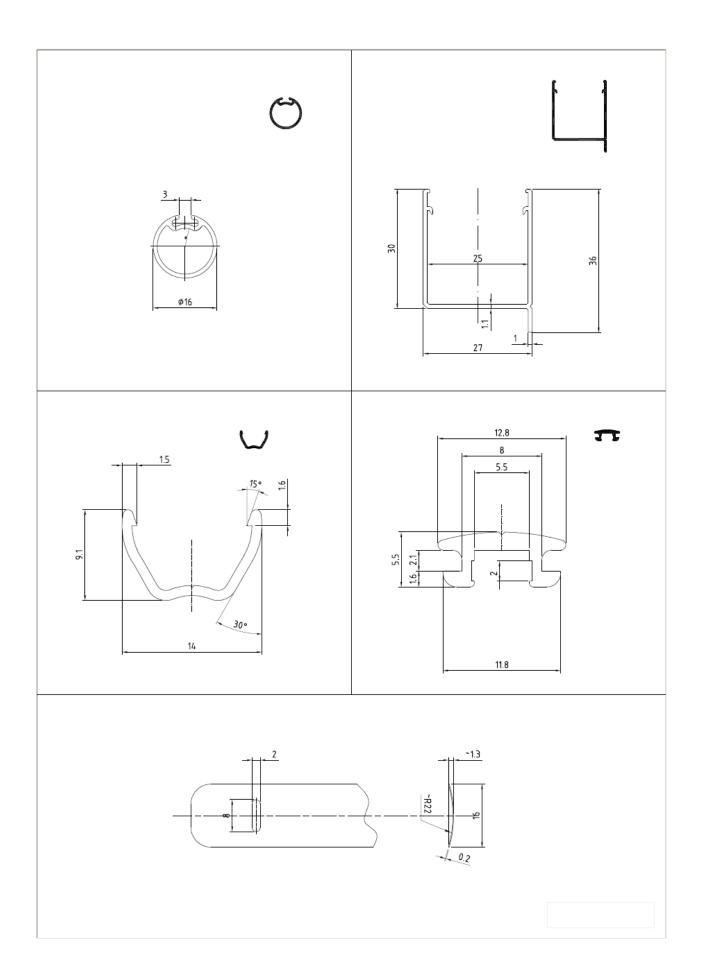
Tube aluminium d'entraînement - Boîtier haut - Eléments constituants la barre de charge - Lamelle store et usinage
